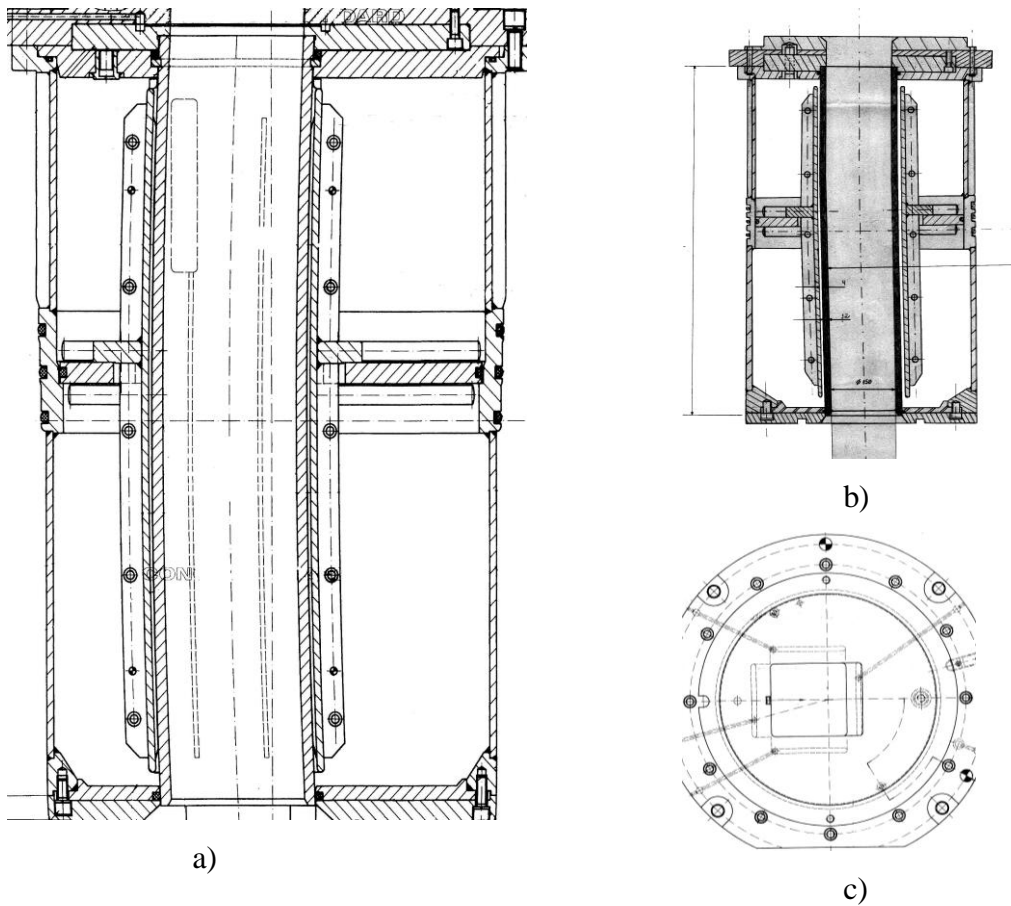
a) Detalhe do molde de seção 150x150 mm, destacando b) o sistema de refrigeração do molde e c) vista de topo.
